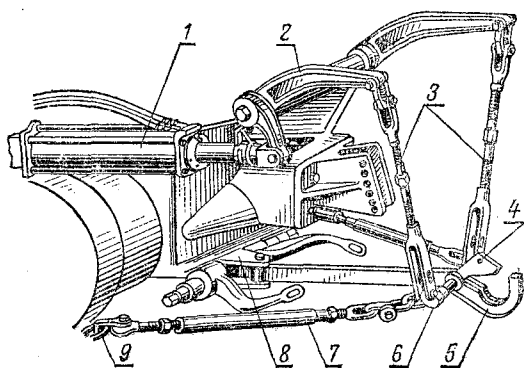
Гидрофицированный крюк трактора Т-40: 1 — силовой цилиндр; 2 — рычаг; 3 — раскосы; 4 — защелка; 5 — крюк; 6 — серьга крюка; 7 — блокировочная тяга; 8 — серьга; 9 — кронштейн.
